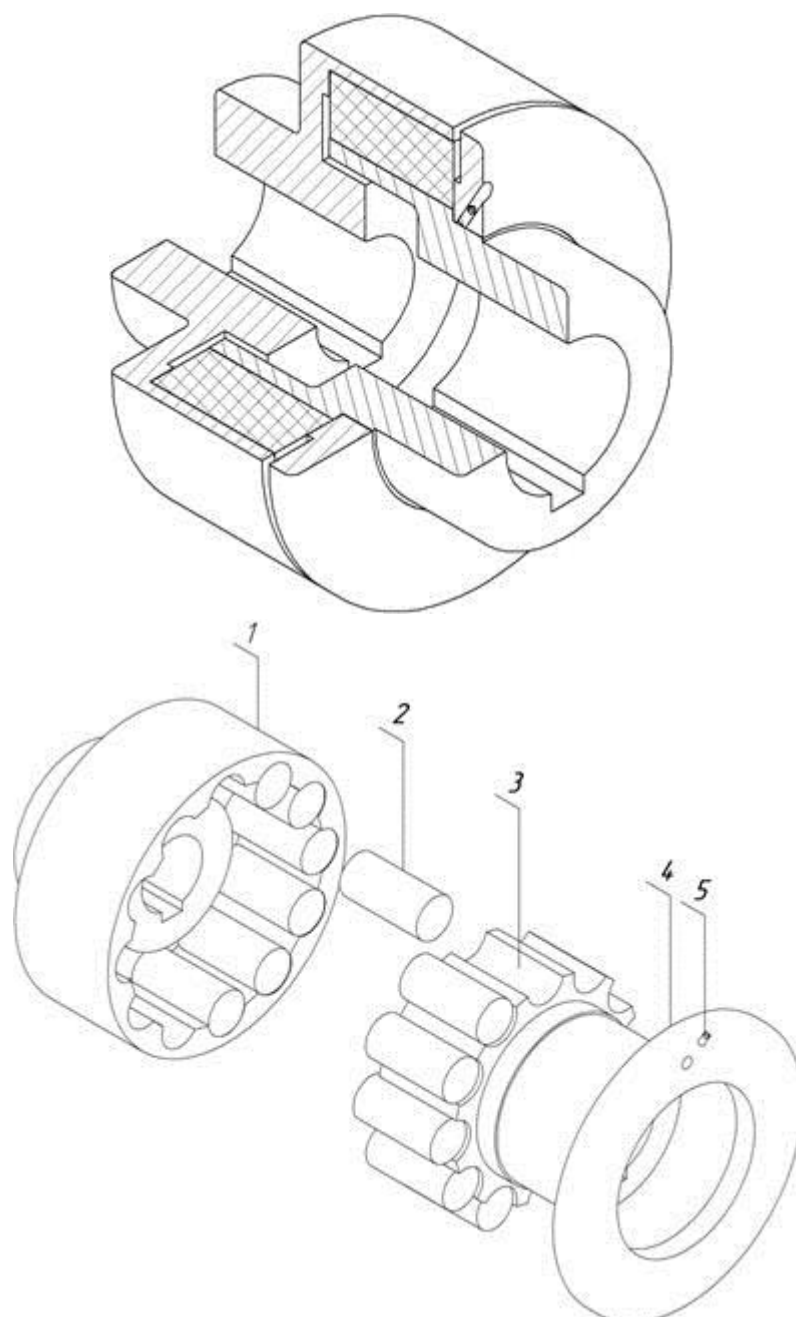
Конструкция муфты с аксиально-расположенными цилиндрическими резиновыми вкладышами
